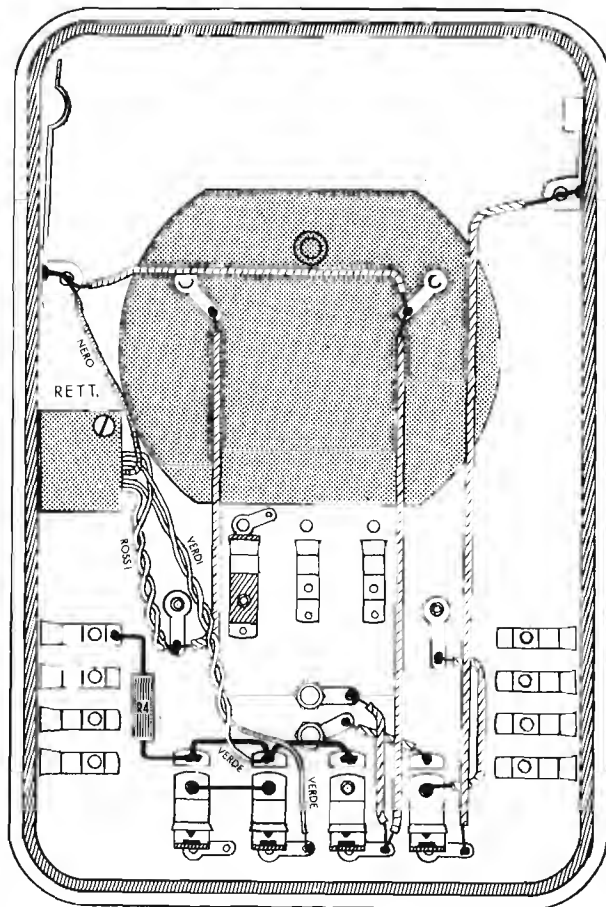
Pannello-supporto con mollette e pagliette per saldatura. Sono indicati i primi collegamenti da eseguire.
